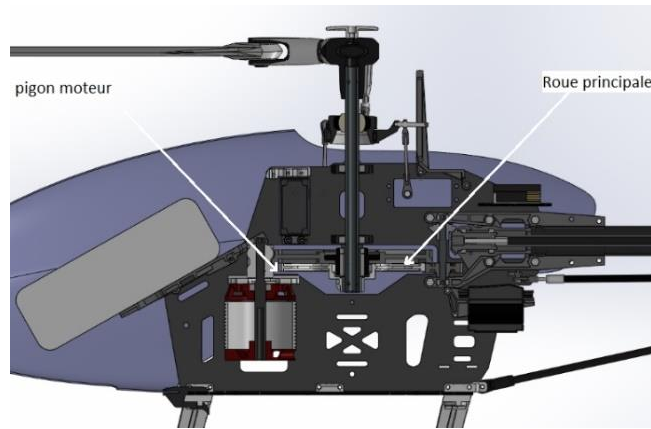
Vue de coupe du châssis montrant le pignon moteur et la roue principale
